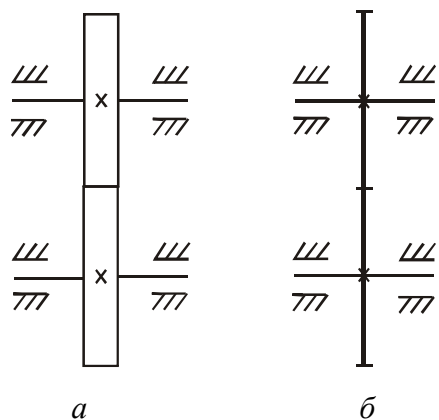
Цилиндрическая передача: а – колеса в зацеплении; б – колеса на кинематической схеме
